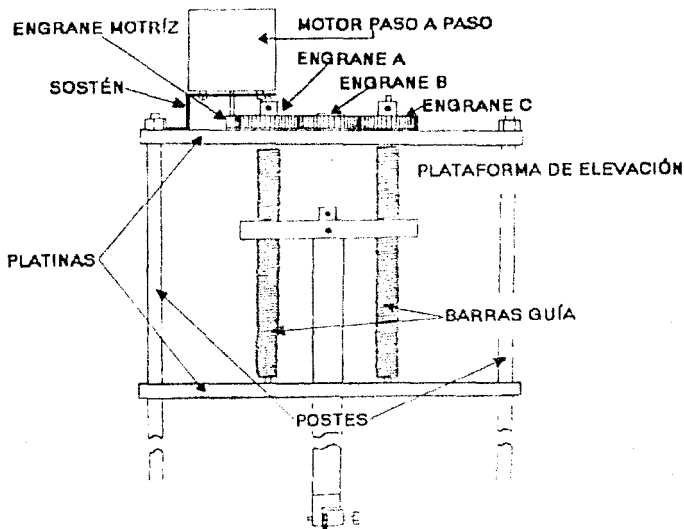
B Sistema mecánico que se encarga de desplazar la semilla fuera del fundente.
